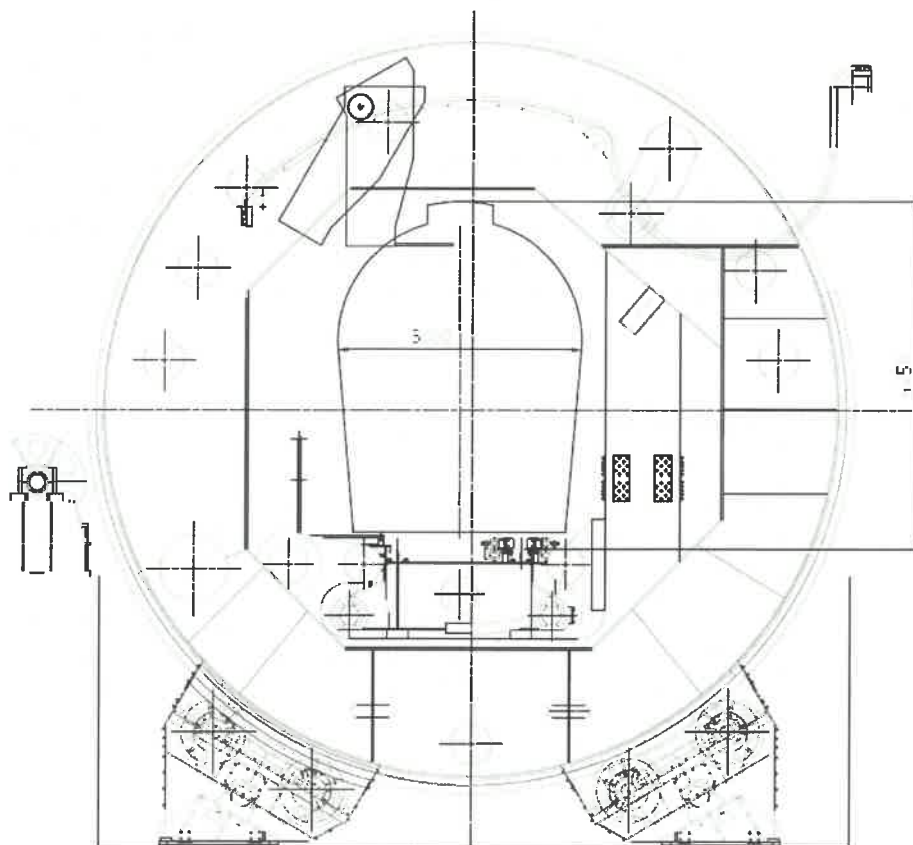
Schemat elementów konstrukcji beczki wywrotnicy wagonowej widok od strony wjazdu
